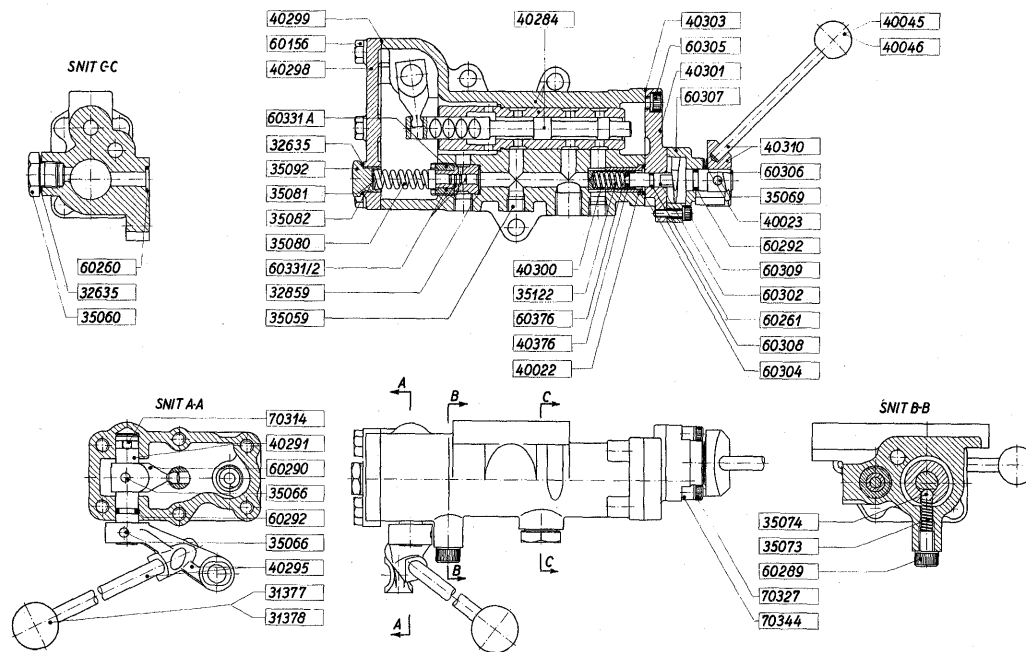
Styreventil - komplet - resv.nr. 40283.
